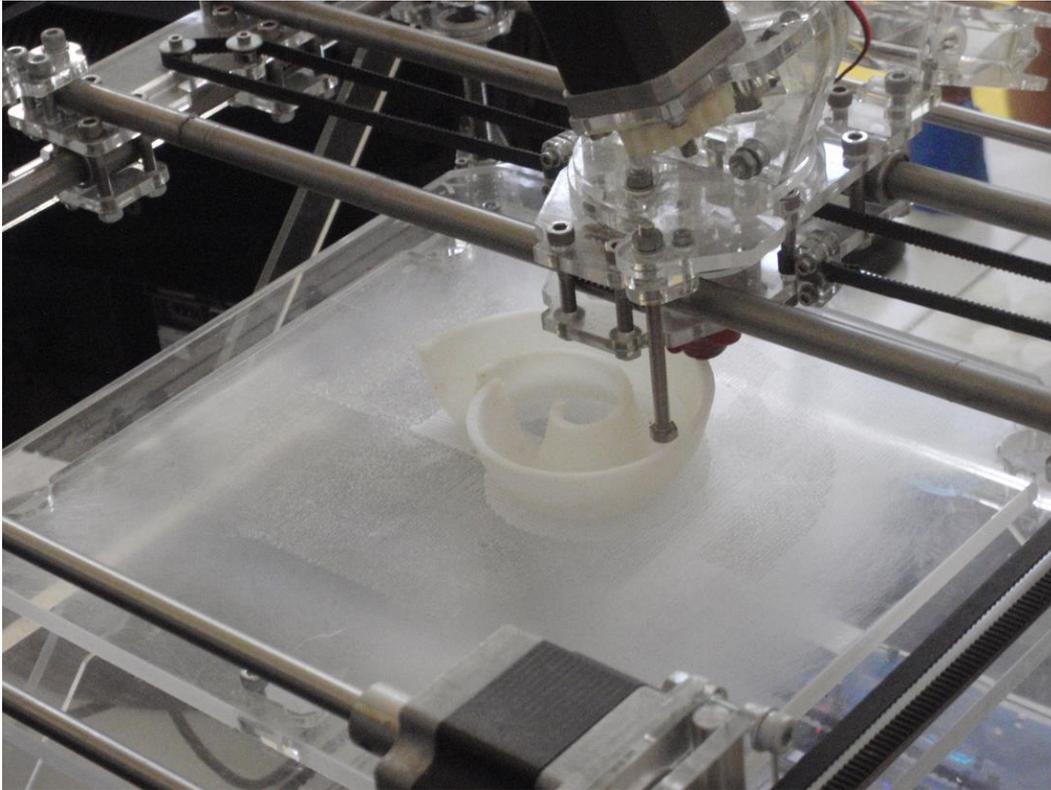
Prototipagem em 3D utilizando impressora por processo de adição. Foto do autor
